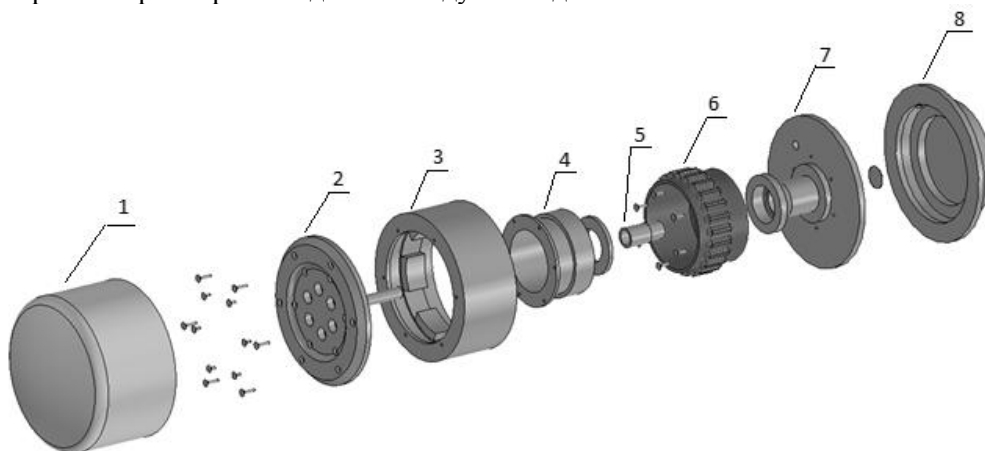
Сборочная трехмерная модель исполнительного органа в разобранном состоянии: 1 – кожух; 2 – вал-диафрагма; 3 – обод с активными частями ротора двигателя; 4 – втулка; 5 – распорная втулка; 6 – статор двигателя; 7 – корпус; 8 – крышка
